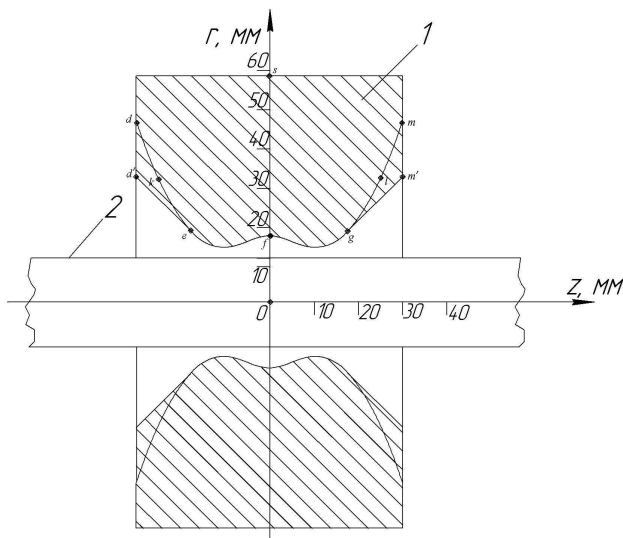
Расчетная конструкция системы массивный одновитковый соленоид – обрабатываемая заготовка: 1 – соленоид; 2 – заготовка
